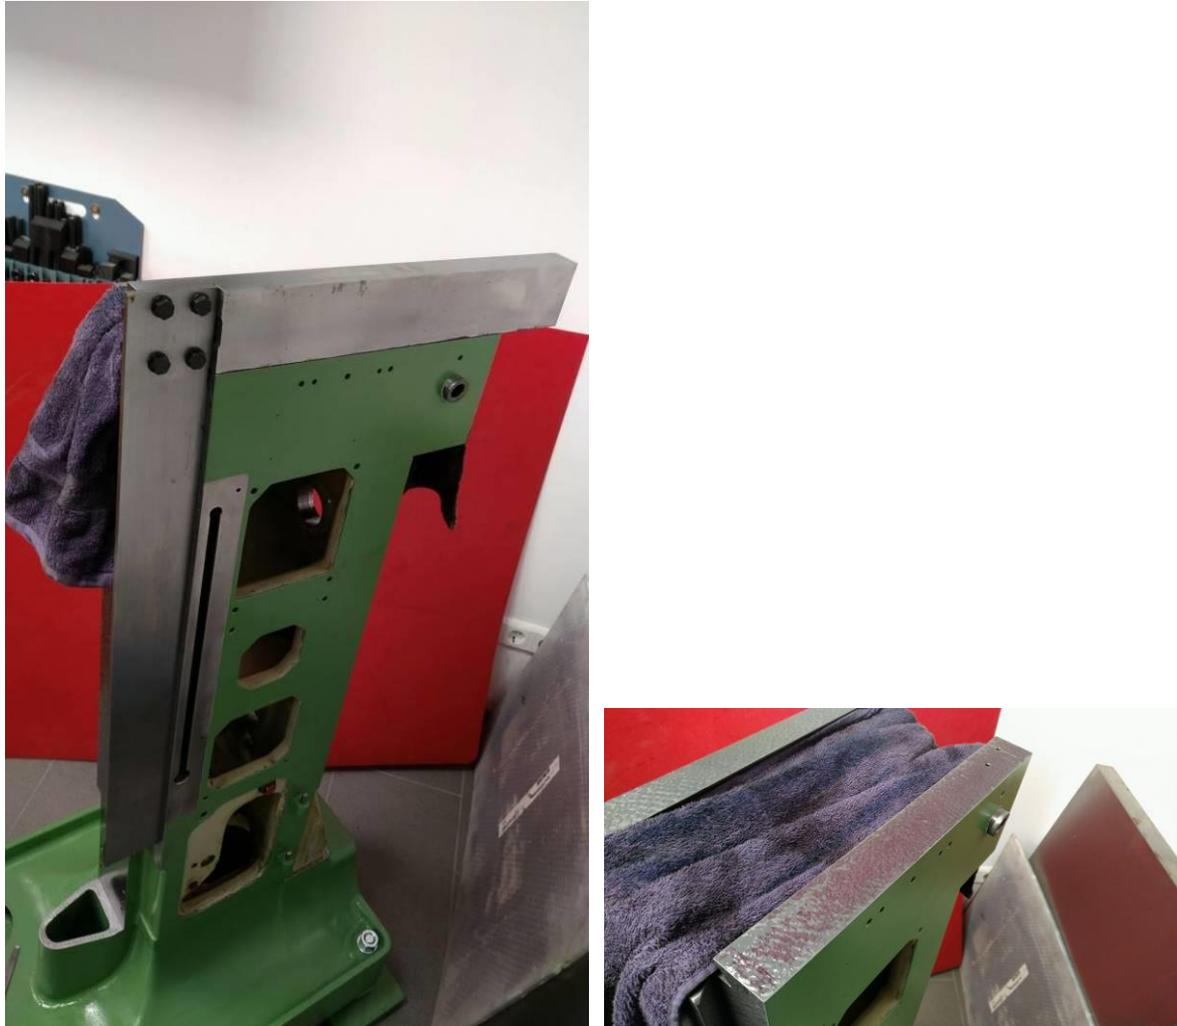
zuerst sicherstellen, dass die Messwerkzeuge ok sind!
